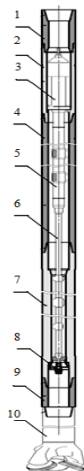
Общее устройство скважинного прибора ТС СИБ-2:
